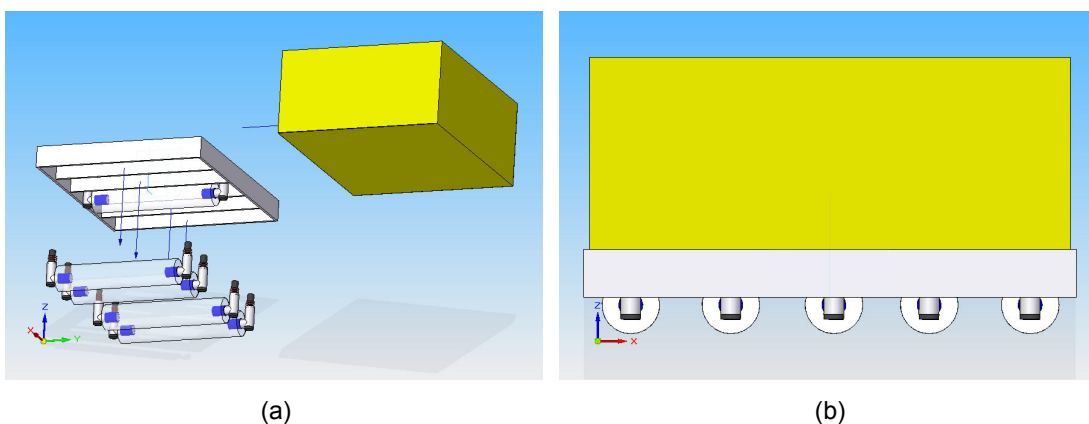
Detalhes da montagem (a) e da disposição dos rolamentos do carro.
